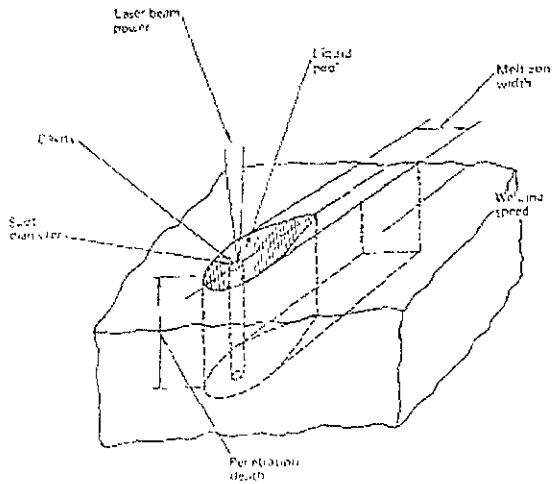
Características de una soldadura de penetración profunda
